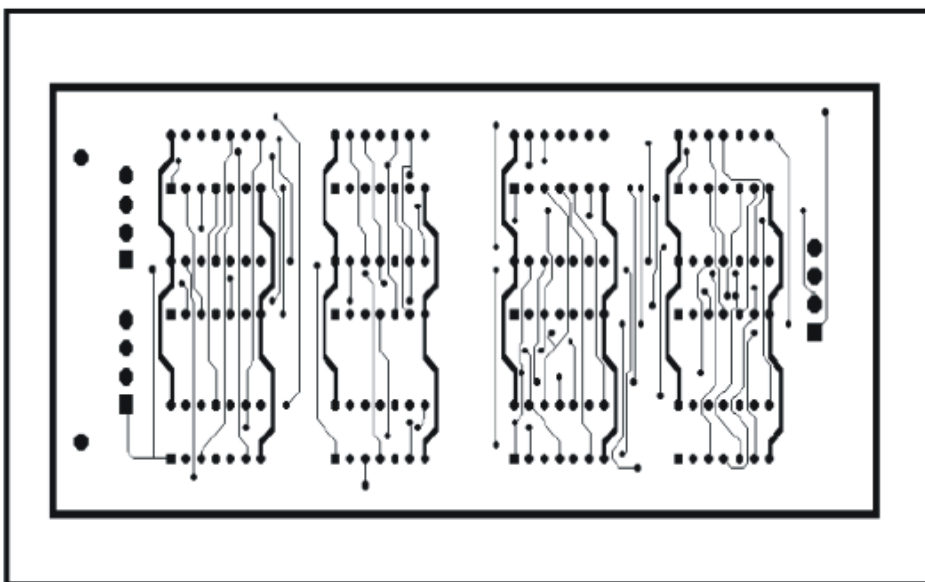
Cara de soldadura (BOTTOM)[40]
